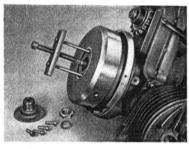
Abziehen des Glockenankers mit Abzieher Nr. 0100031. Beide Zugschrauben ganz einschrauben! Besser Abzieher Nr. 0100033 verwenden (s. Bild 211)
